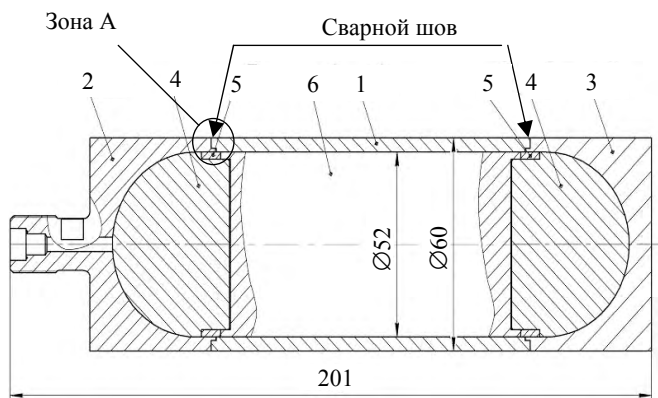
Конструкция прочностного макета из стали 12Х18Н10Т: 1 – обечайка; 2, 3 – крышка; 4, 6 – вкладыш; 5 кольцо
